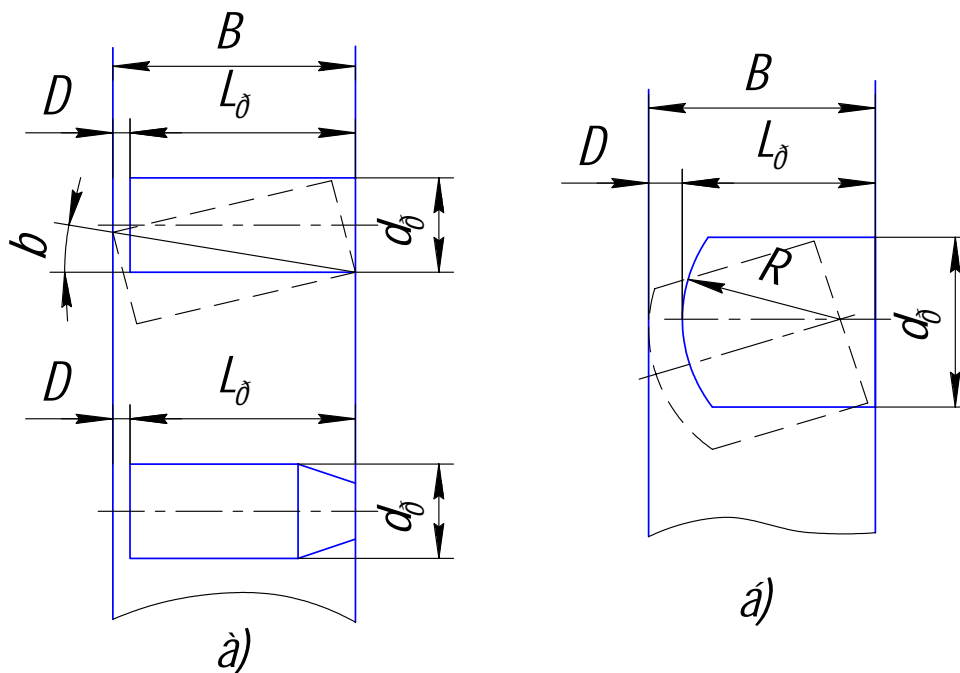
Схема для розрахунку проходження заготовок у лотках
